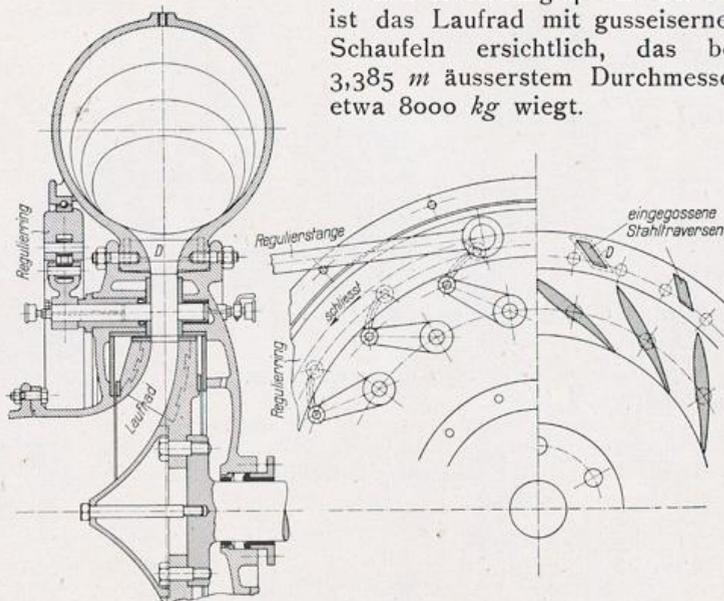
Spiral-Francis-Turbine für Schwyz.
